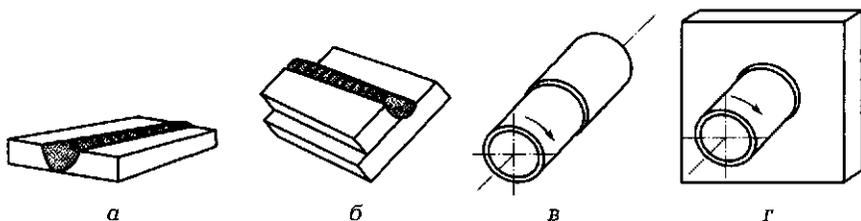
Положение при сварке стыковых и тавровых швов:
